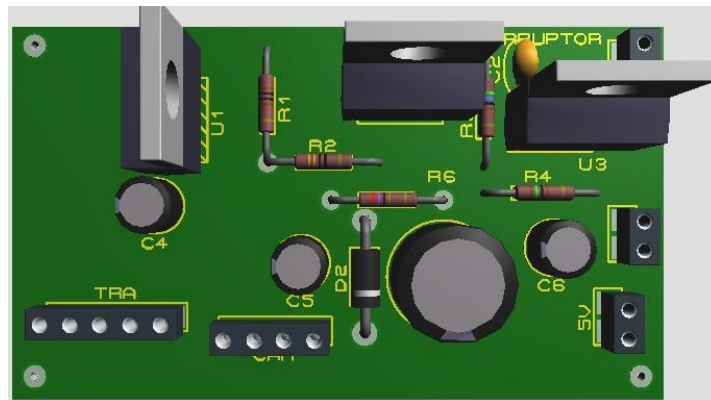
Placa PCB en 3D del Circuito de alimentación robot
